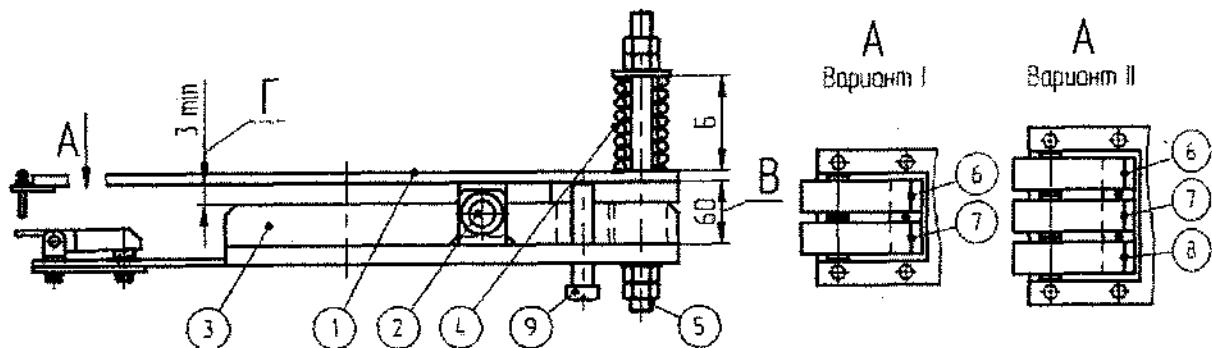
Механическое взвешивающее устройство: 1 - опора; 2 - ось; 3 - качалка; 4 - пружина; 5 - тяга; 6, 7, 8 - микровыключатель; 9 - болт.
